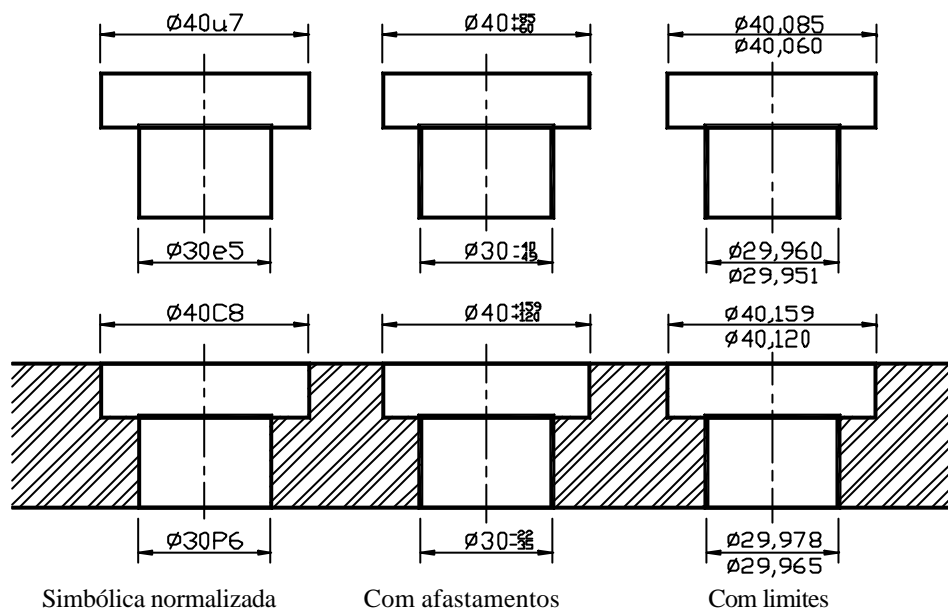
Exemplo de indicação de tolerância dimensional para eixo e para furo
